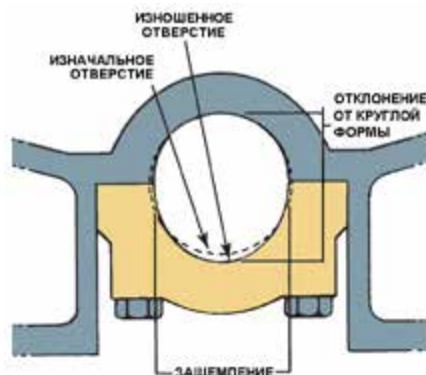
Если крышки коренных подшипников испытывают изгибающую нагрузку направленную вниз, коренные подшипники зажимаются вдоль разделительной линии; источник: *Pearson Education, Inc.
